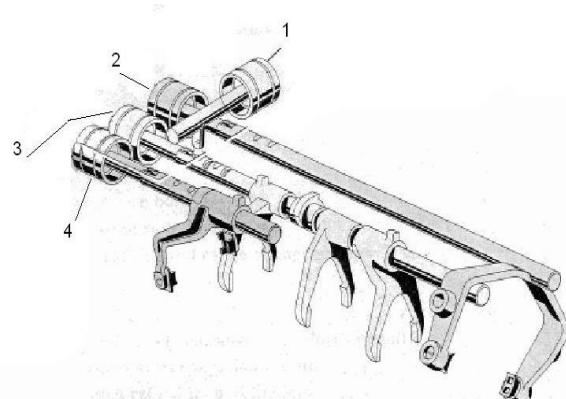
Механизм управления коробкой передач ZF 16AS2601: 1 – исполнительный механизм выбора основной КП; 2 – исполнительный механизм демультиплексора; 3 – исполнительный механизм включения основной КП; 4 – исполнительный механизм управления делителем
